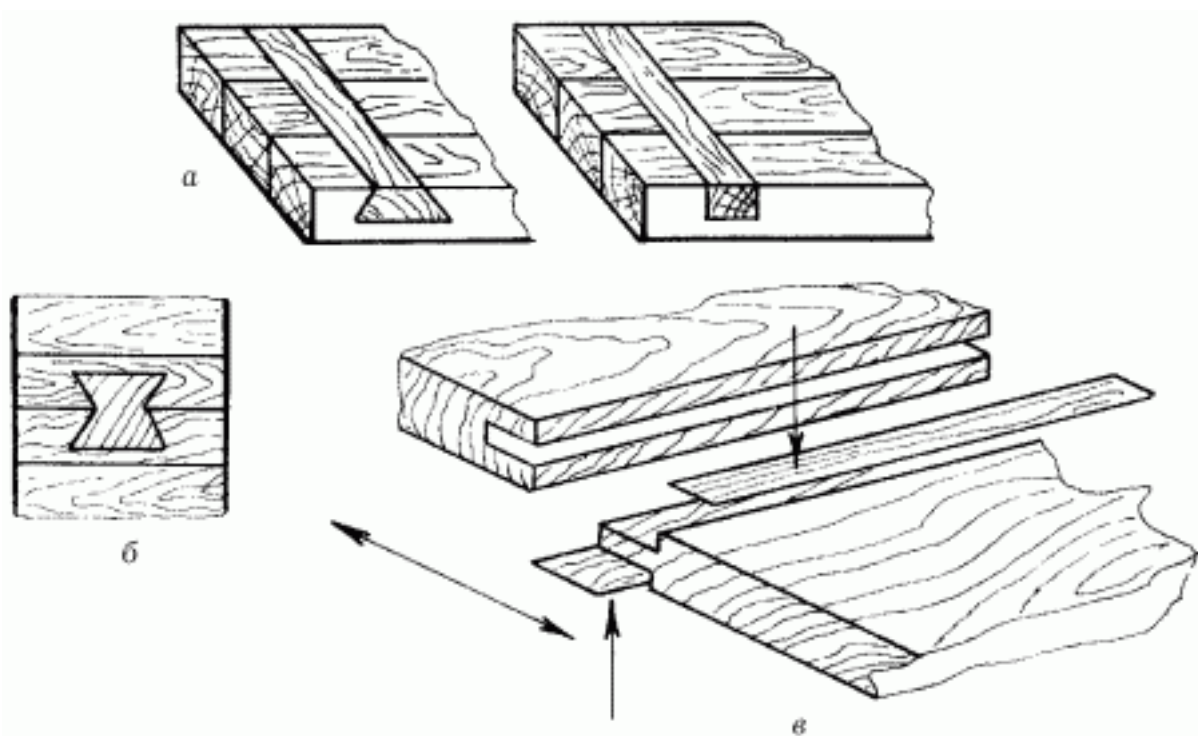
Укрепление соединений на гладкую фугу: а – шпонками; б – вставными шипами; в – вставными пластинами шпона.
